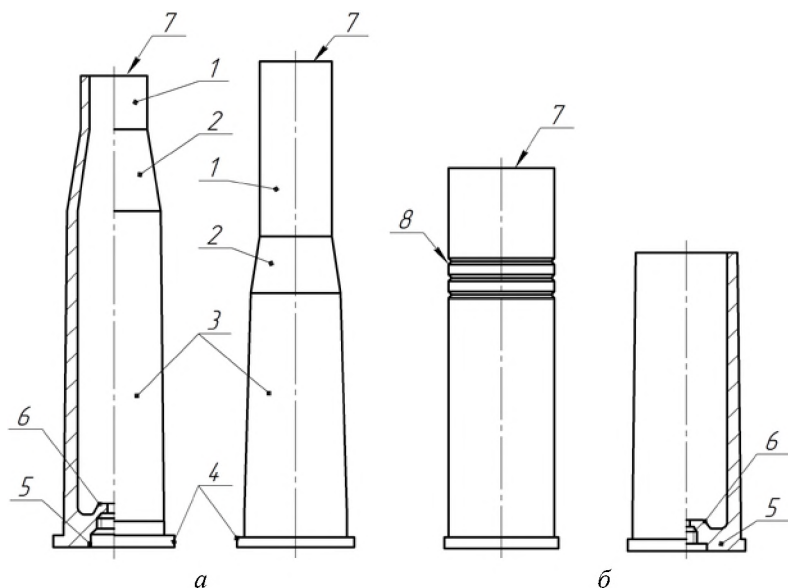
Конструктивные элементы гильз: *а* – бутылочной формы; *б* – цилиндрической формы; 1 – дульце; 2 – скат; 3 – корпус; 4 – фланец; 5 – дно; 6 – сосок; 7 – дульце (срез); 8 – обтюрирующая канавка
